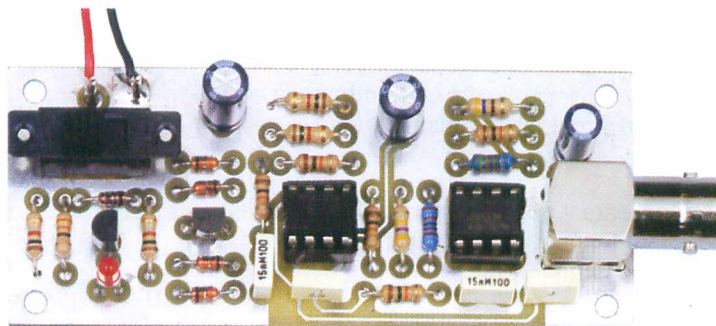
Foto del montaggio del calibratore LX.1691. A sinistra è visibile il corpo dell'interruttore di accensione e, a destra, quello del connettore BNC di uscita.
